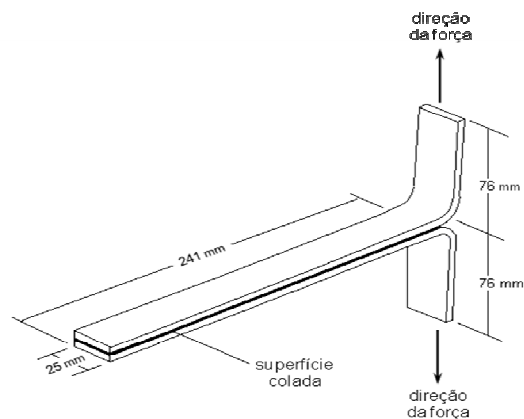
Esquema do corpo de prova com dimensões recomendadas para o ensaio.
